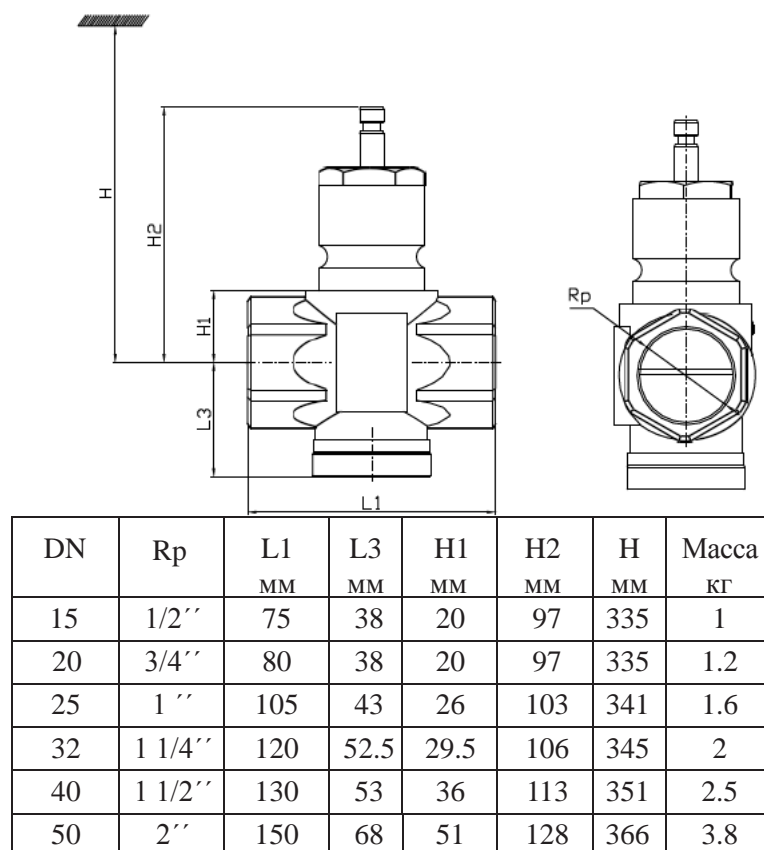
Внешний вид и габаритные размеры двухходового муфтового клапана
